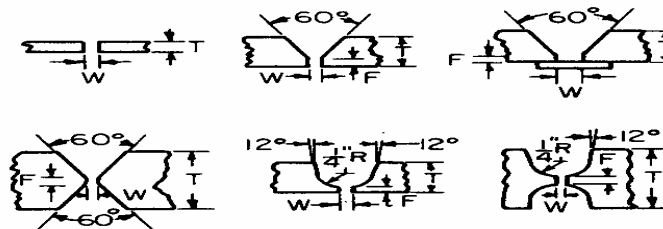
Soldaduras de ranura para soldadura manual de arco metálico protegido. Las dimensiones en pulgadas se muestran en la tabla inmediatamente abajo.
